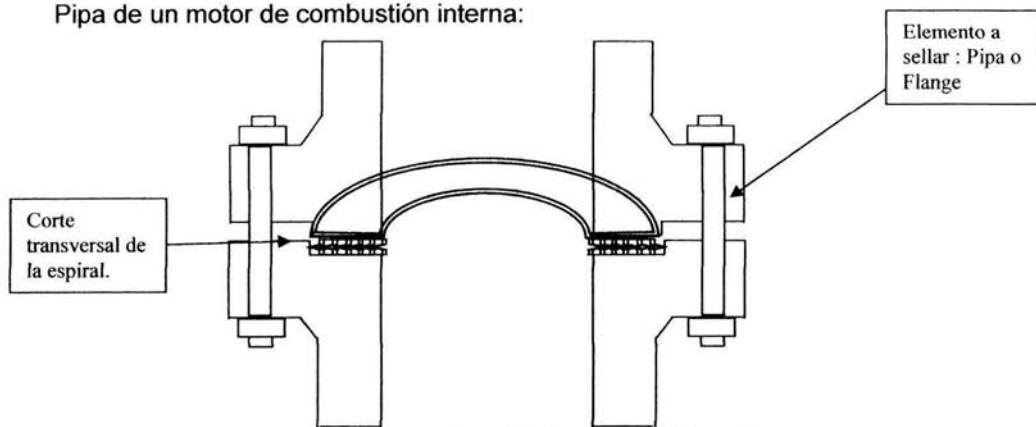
Ensamble de espiral en la Pipa o Flange.
